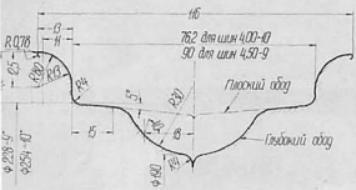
Профиль обода для шин 4.00-10 и 4.50-9.
